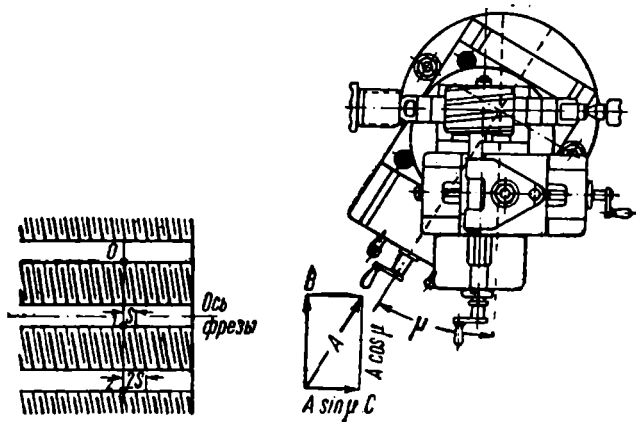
Гребенка и приспособление для затылования резьбовых фрез по профилю.
